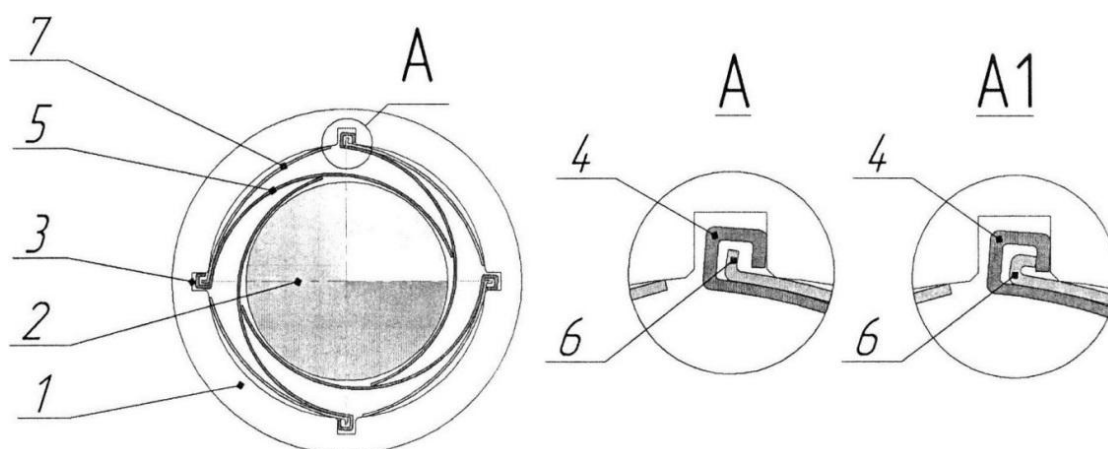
Радиальный лепестковый газодинамический подшипник
